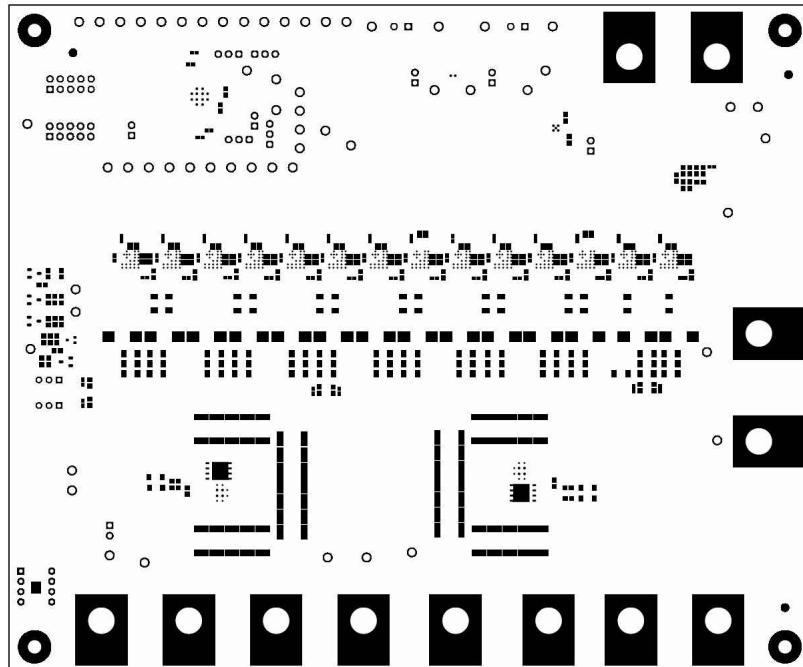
TPS53676EVM-084 PCB 底部焊接
